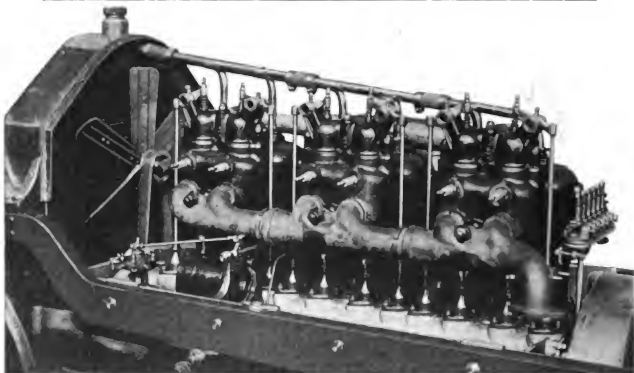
und 6. Sechszylindermotor mit gepaarten Zylindern und hängenden, von oben gesteuerten Saugventilen, gebaut von A. Horch in Zwickau i. S.
